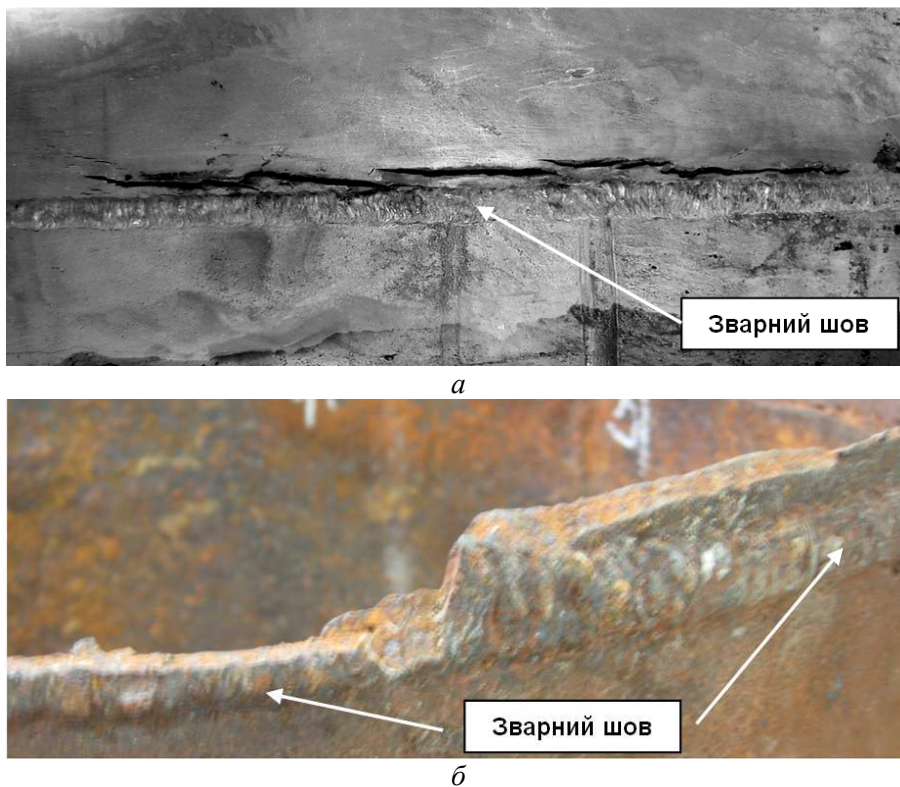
Типові приклади корозійно-механічного руйнування зварного з'єднання від зовнішньої поверхні у повздовжньому шві (а) та від внутрішньої поверхні у кільцевому зварному шві (б)
